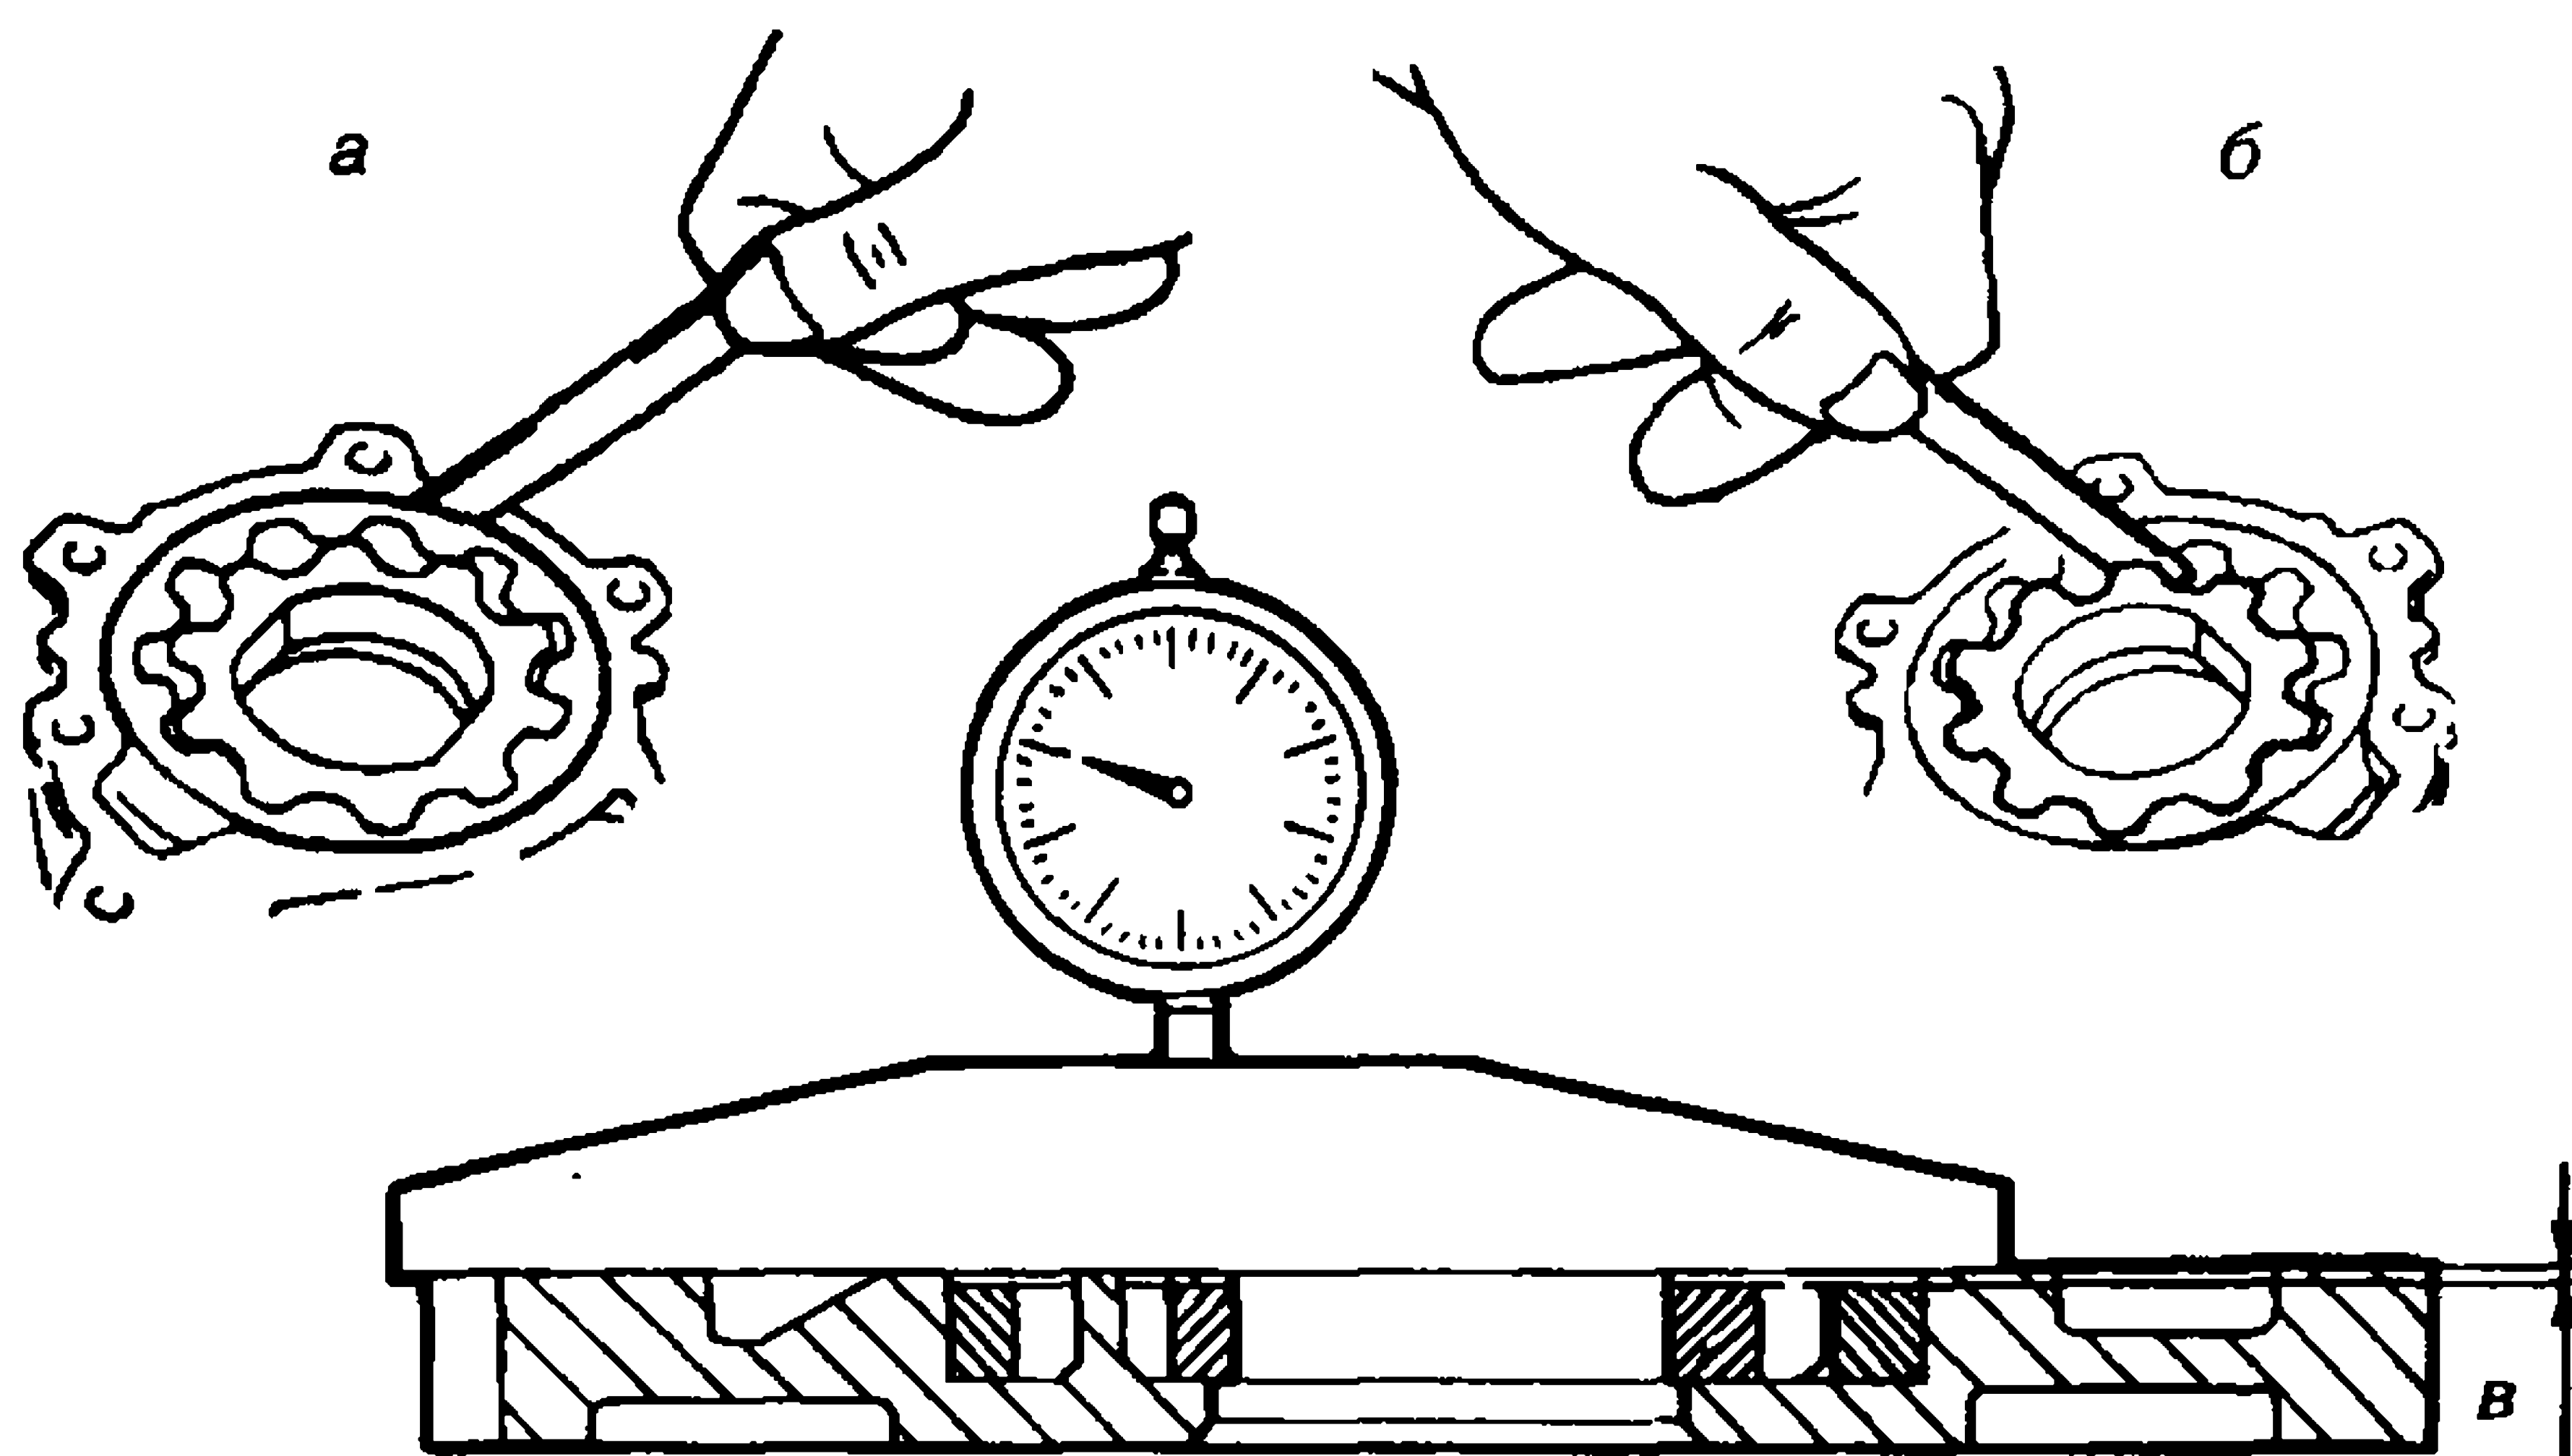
Проверка зазоров (двигатели 1111, 11113, 2108, 21081, 2110):
